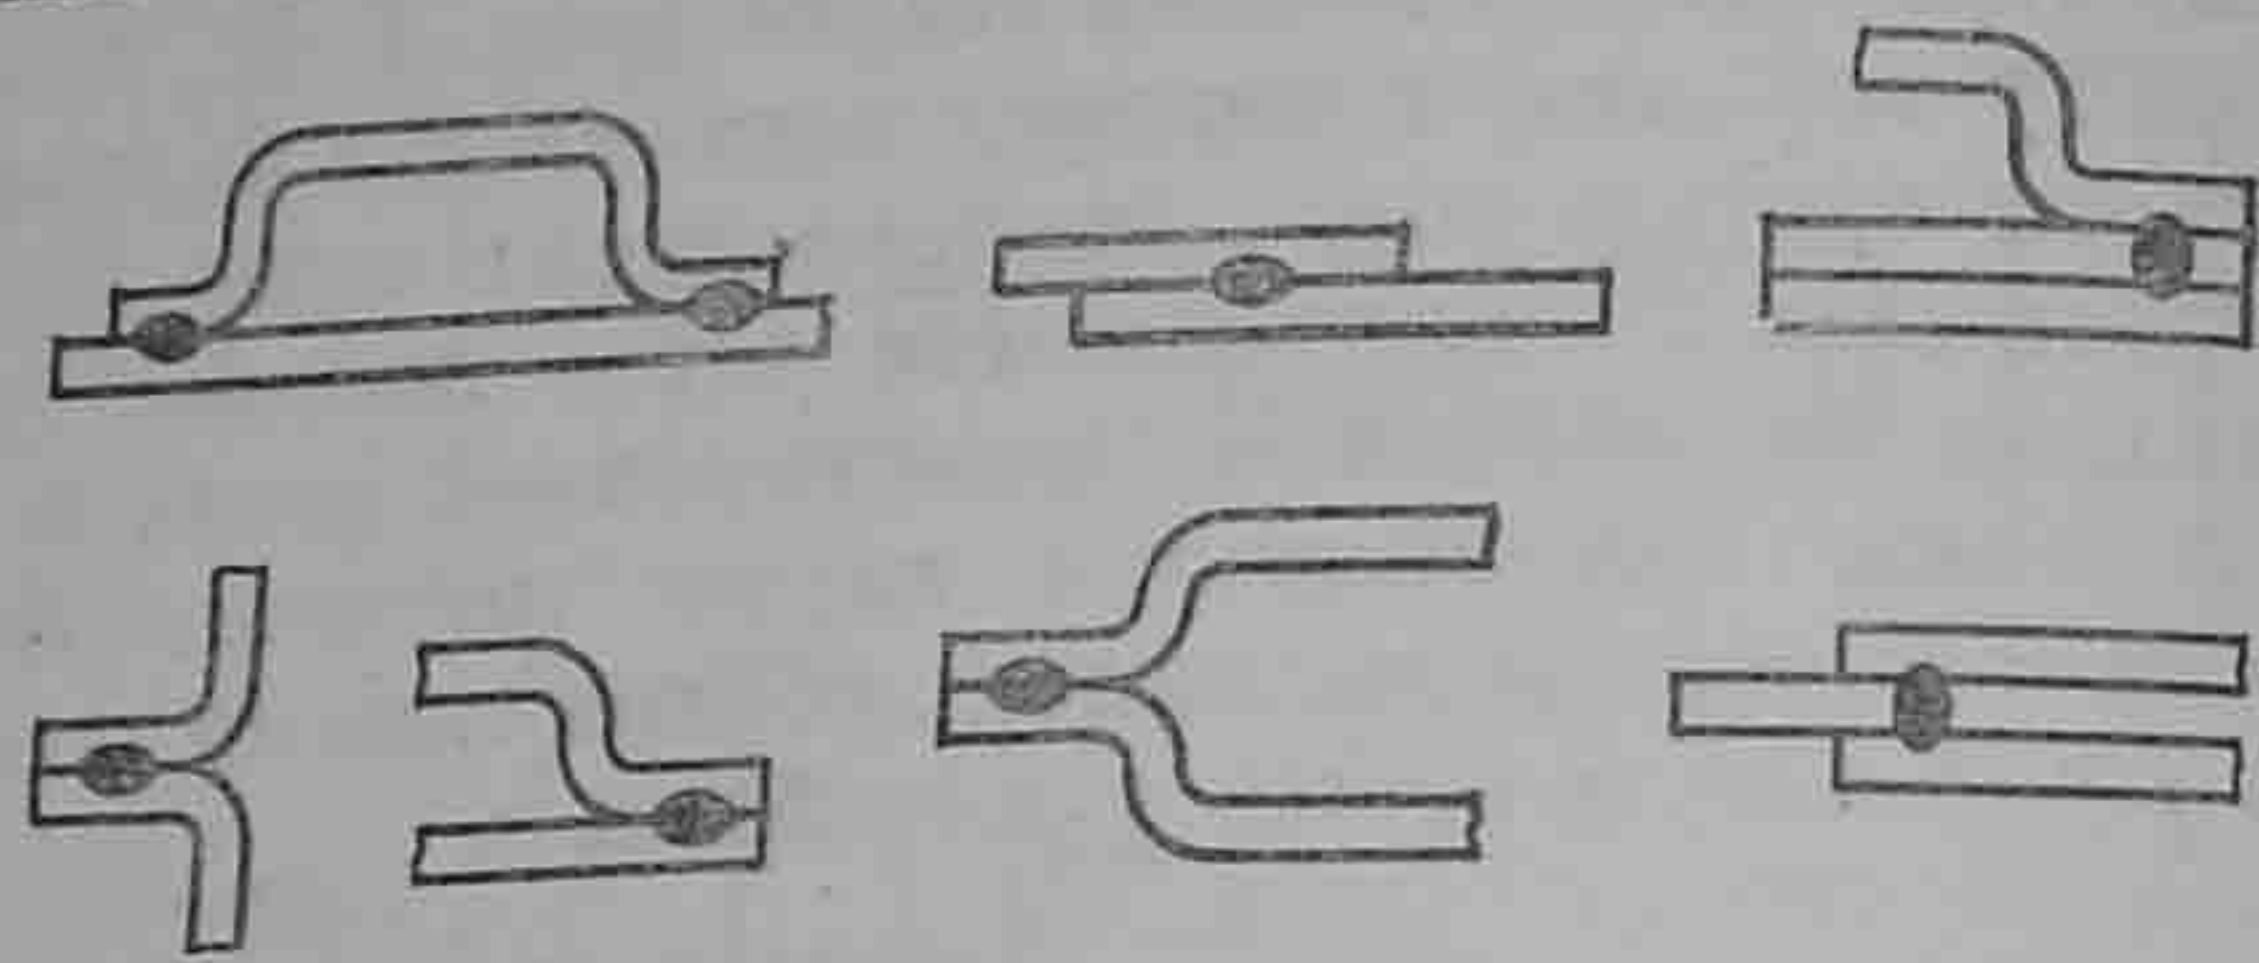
Типы сварных соединений точечной сварки
